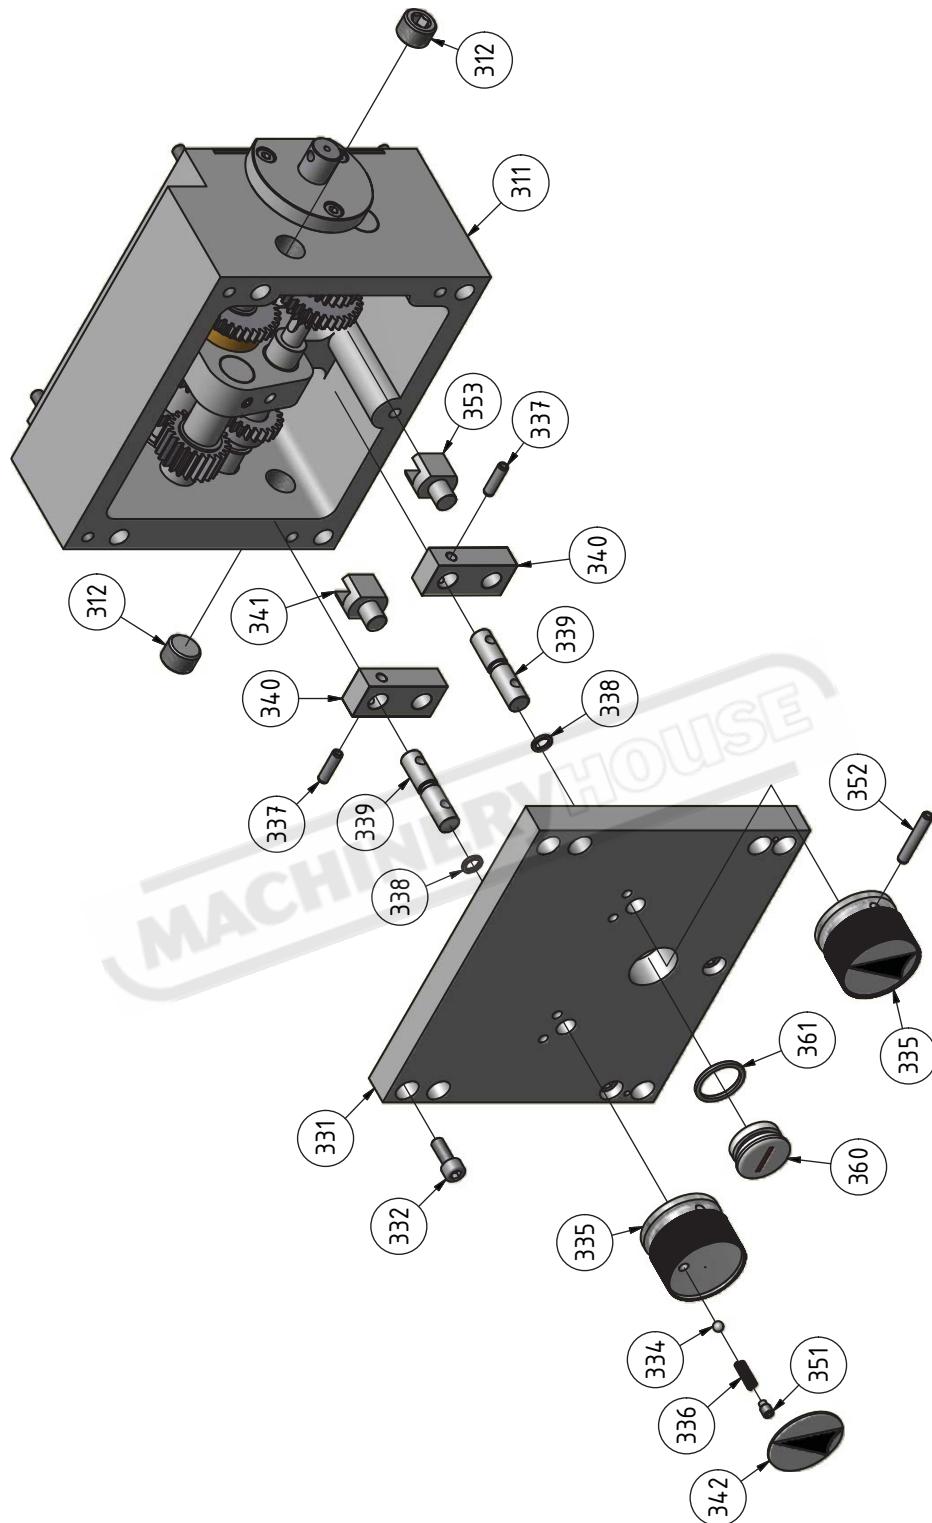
Vorschubgetriebe 1 von 2 - Feed gear 1 of 2 - TU2807
